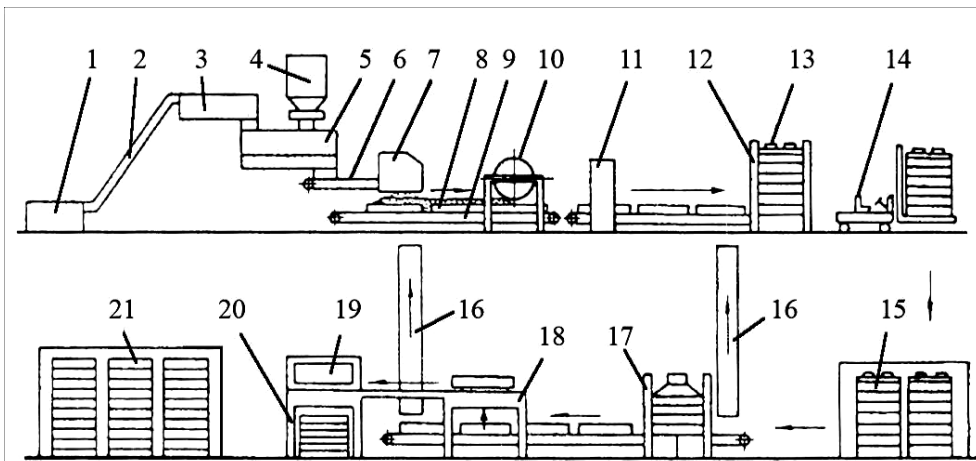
Технологічна схема виготовлення фібролітових плит:
